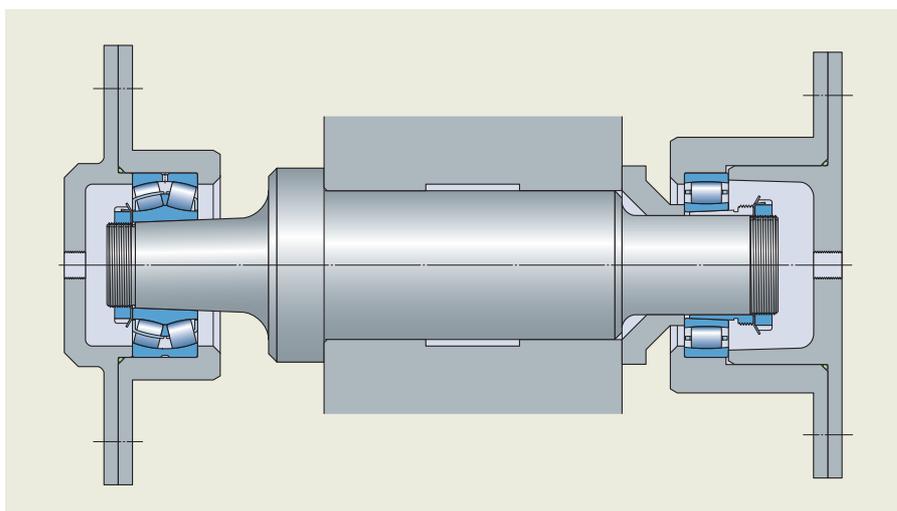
Propuesta de SKF con un rodamiento de rodillos a rótula y un rodamiento de rodillos toroidales CARB
